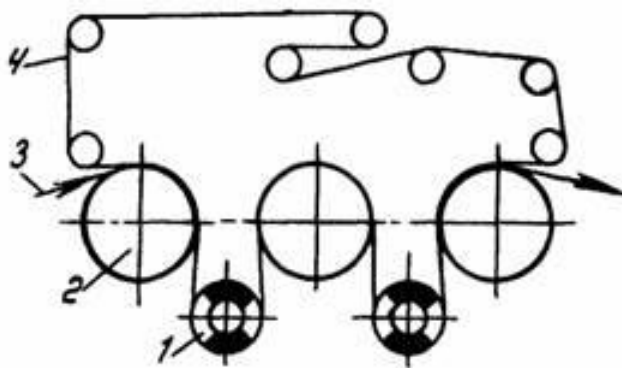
Однорядна компоновка сушильних циліндрів з вакуумними валами: 1 – вакуумний вал; 2 – сушильний циліндр; 3 – паперове полотно; 4 – сушильна сітка
